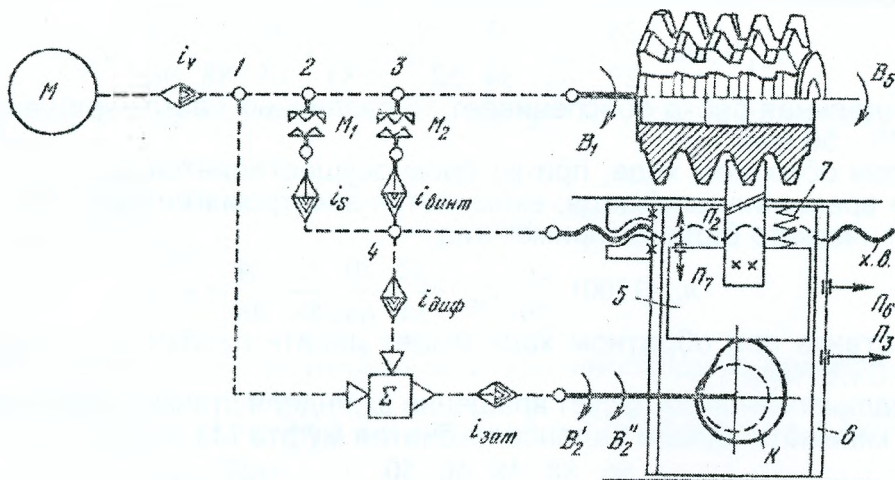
Кинематическая структура зубозатыловочного станка:
